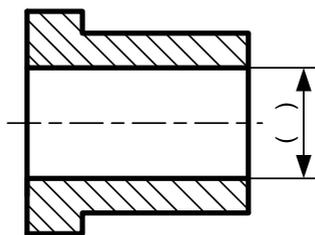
Обозначения при обработке отверстий на сборочном чертеже
